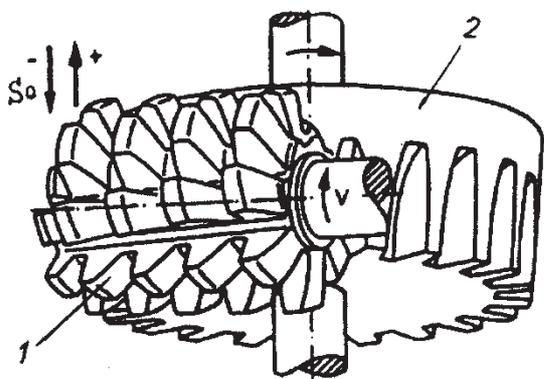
Принцип образования зубьев цилиндрических колёс червячной фрезой
